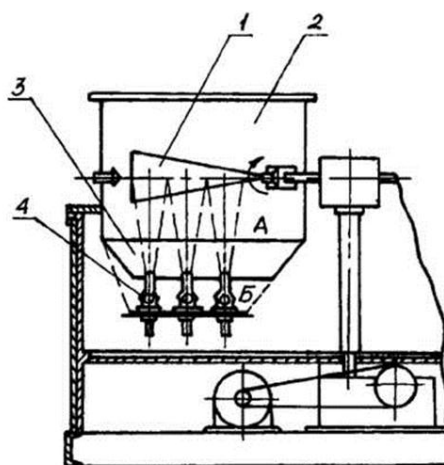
Схема камеры гидродробеструйной установки
